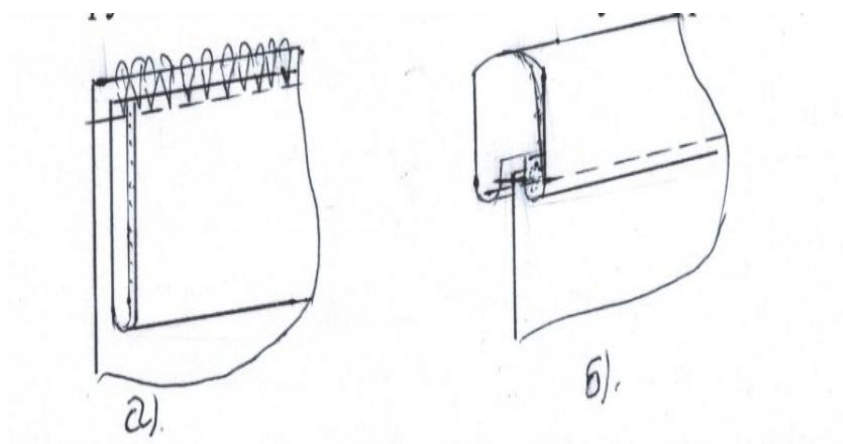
Варіанти з'єднання манжет з рукавами: а).зшивний шов; б).
